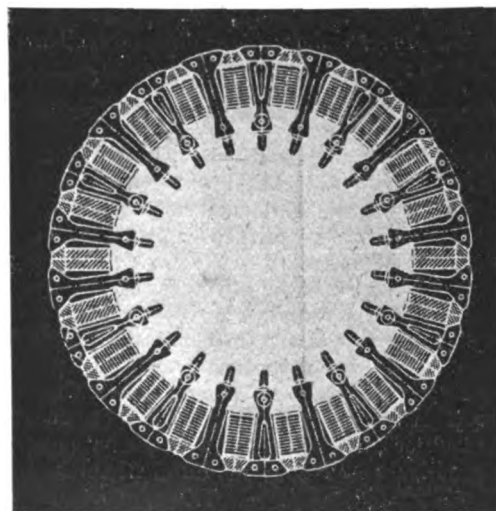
Coupe d'un rotor d'alternateur de l'A. E. G.
